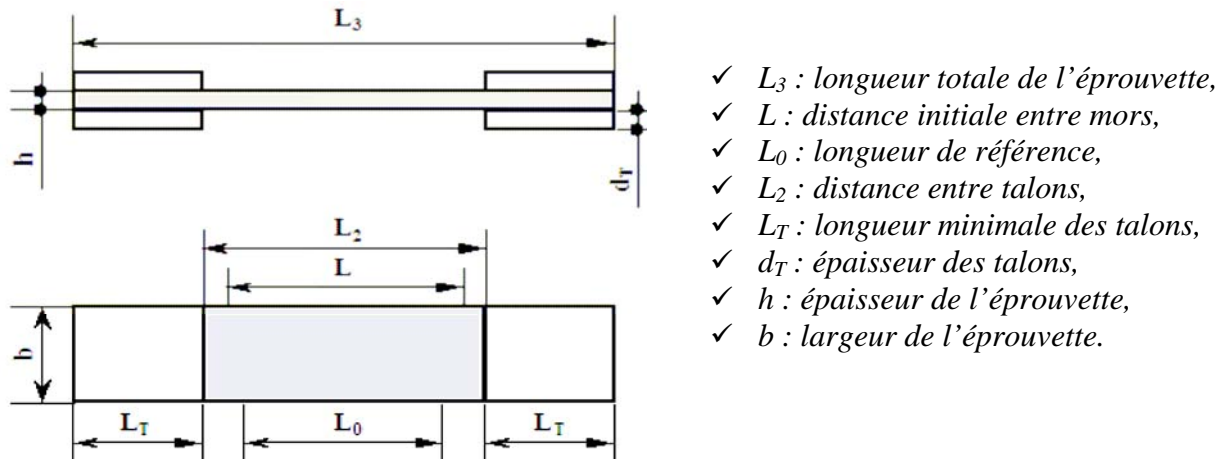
Dimensionnement des éprouvettes de traction
